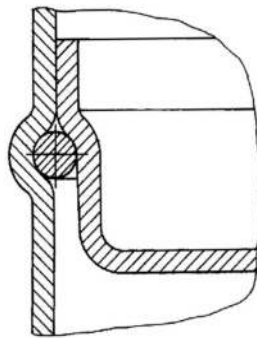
Схема опорного пристрою згідно з пат. № RU2033234C1
